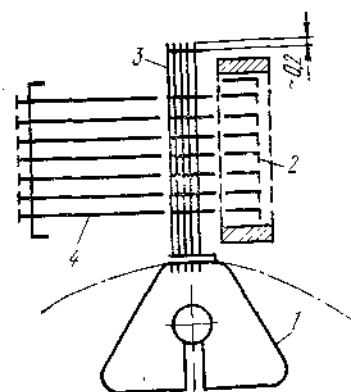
Дополнительный игольный прибор (продольный разрез):
